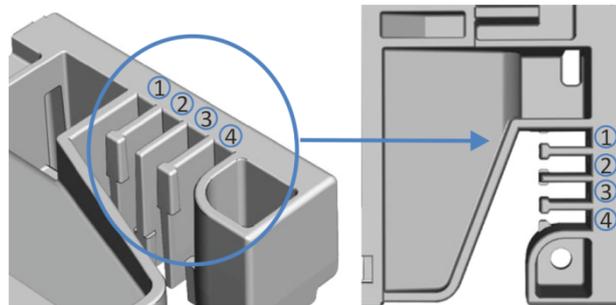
Schlauchkanal mit Schlauchführungen (links: Ansicht von innen, rechts: von oben)
